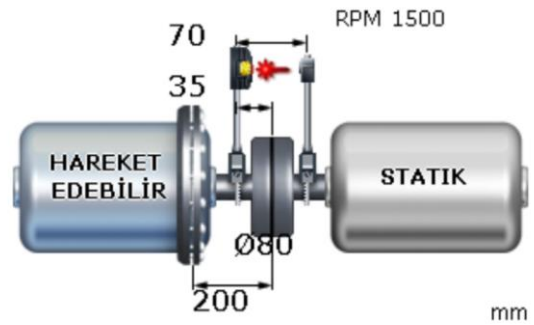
Pruftechnik Shaftalign OS3 motor mili hizalama cihazı
